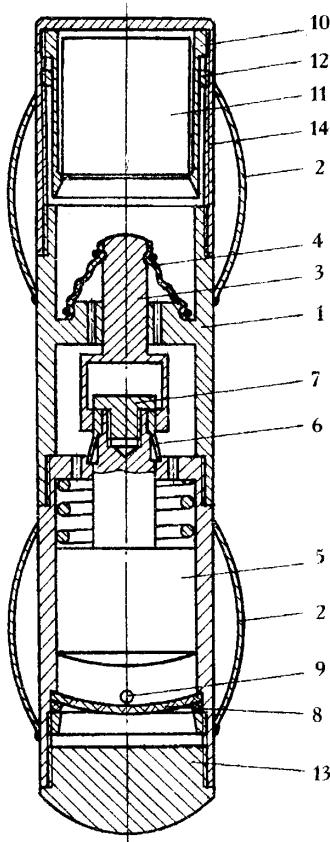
Пристрій для вимірювання зенітного кута свердловини вкидного типу КВ-295: 1 - корпус; 2 - пружини центрувальні; 3 - шток; 4 - компенсатор зміни об'єму; 5 - ступінчастий поршень; 6 - фіксатор; 7 - фігурний гвинт; 8 - сферична шкала; 9 - кулька; 10 - утримувач; 11 - вантаж; 12 - упорна втулка; 13 - заглушка; 14 - корпусний стакан
